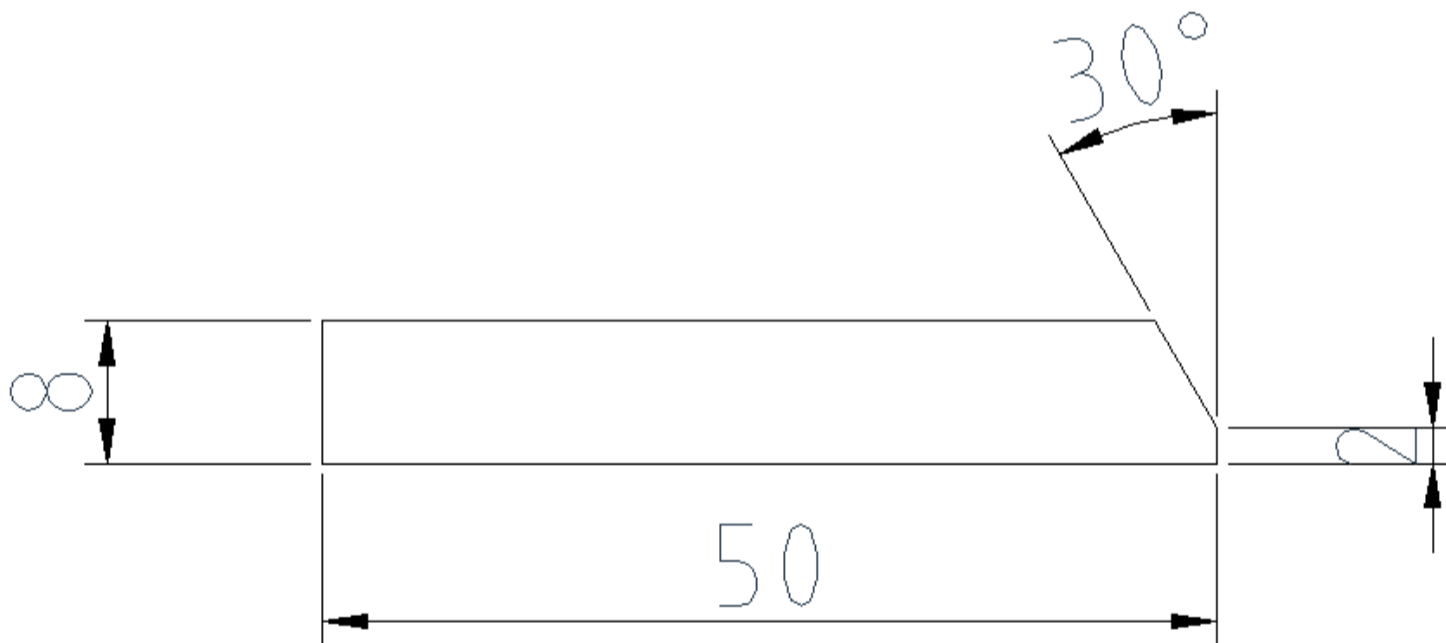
Medidas en milímetros de la junta de placas para ser soldadas
